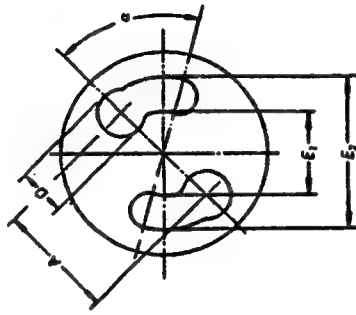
Dimensioni del portastarter destinato a ricevere soltanto starter per apparecchi di illuminazione della Classe II
